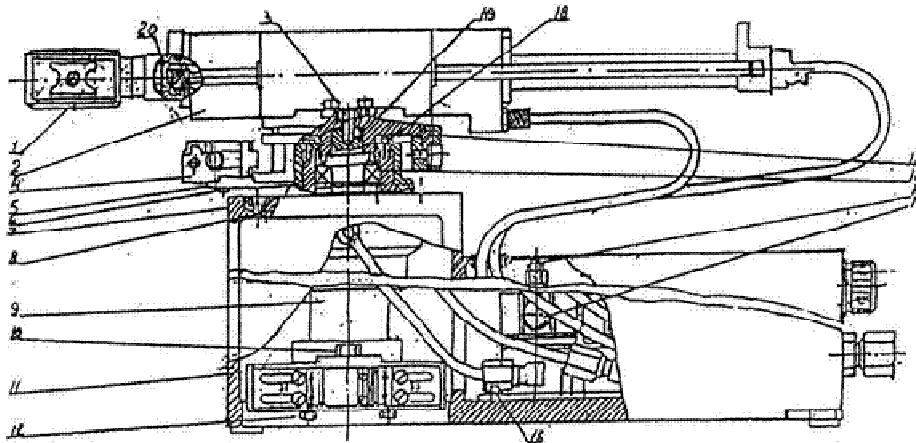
Головний вид: 1 - схват; 2 - рука; 3 - болт; 4 - амортизатор поворота; 5 - кривинний; 6 - квіт; 7 - кривий; 8 - квіт; 9 - механізм підйому; 10 - шпилька; 11 - механізм поворота; 12 - болт; 13 - шпилька; 14 - узел розподілення; 15 - дросель; 16 - підшипник; 17 - муфта з упором; 18 - квіт; 19 - квіт; 20 - сигнальний вузол контактів
